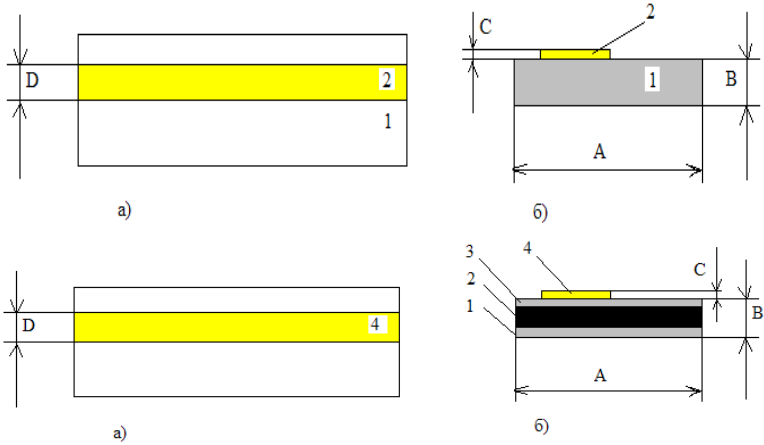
Ленточный плакированный материал, содержащий полосу серебра (для корпусов КТ-26, КТ-89, КТ-92–а) (а) вид сверху; (б) поперечное сечение: 1– основа –медный сплав; 2– полоса серебра; (для корпуса КТ-27 (а) вид сверху; (б) поперечное сечение: 1– медь; – основа – сталь 08КП; 3– медь; 4– полоса серебра
